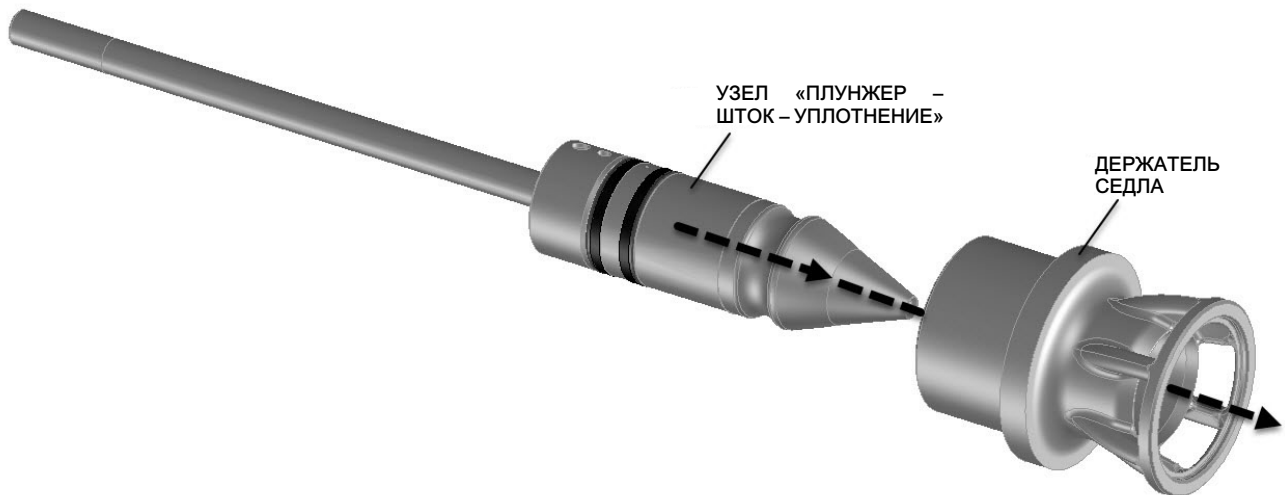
Узел клапана ССV с NPS 4 — Установка узла «плунжер – шток – уплотнение» через нижнюю часть держателя седла
